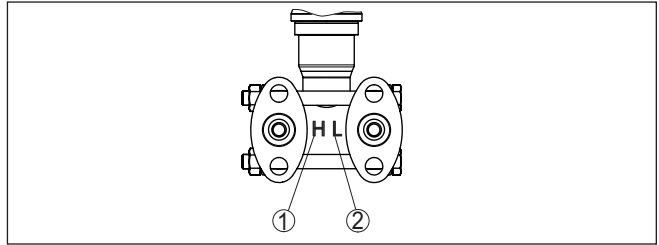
Kennzeichnung für Hoch-/Niederdruckseite an der Prozessbaugruppe
